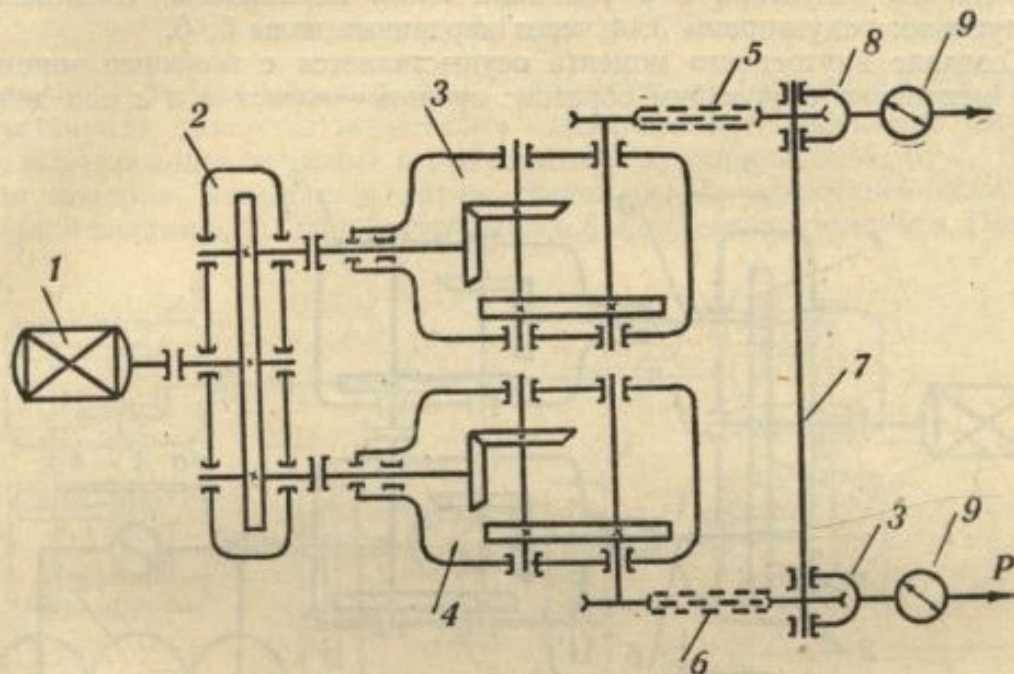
1 — Электродвигатель, 2 — цилиндрический редуктор, 3, 4 — испытуемые редукторы, 5, 6 — втулочно-роликовая цепь, 7 — промежуточный вал, 8 — подвижные опоры, 9 — динамометр.
